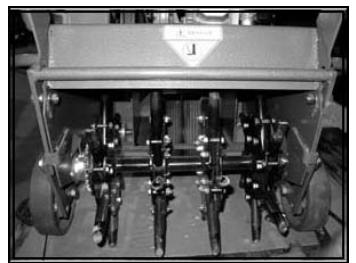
Il rotore cadrà quando i gruppi cuscinetti sono rimossi.
